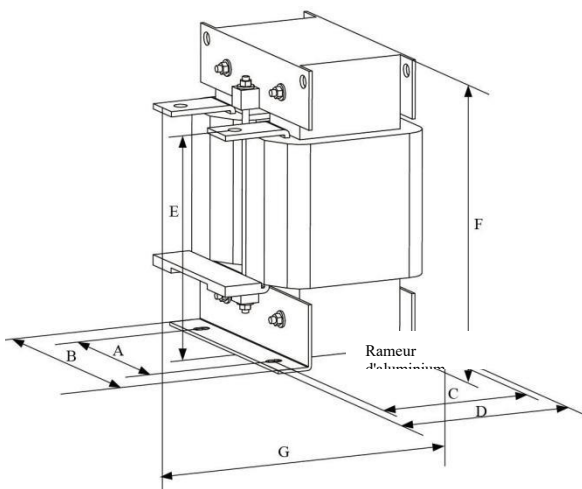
Dessin dimensionnel du réacteur CC externe
